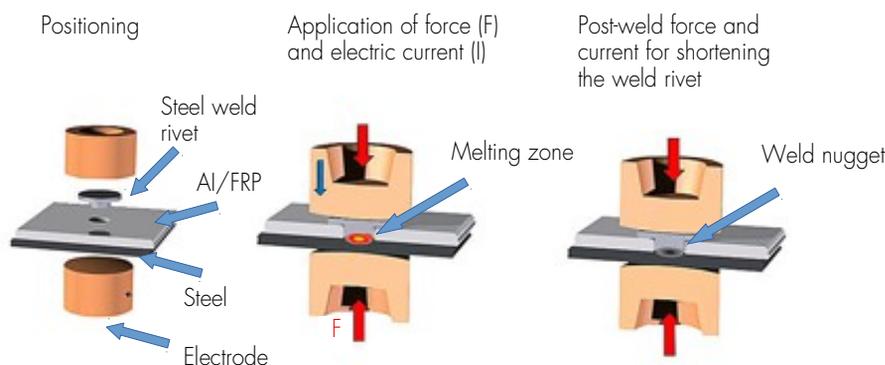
soudage par élément de résistance (source: Laboratory of Materials and Joining Technology, Université Paderborn)
